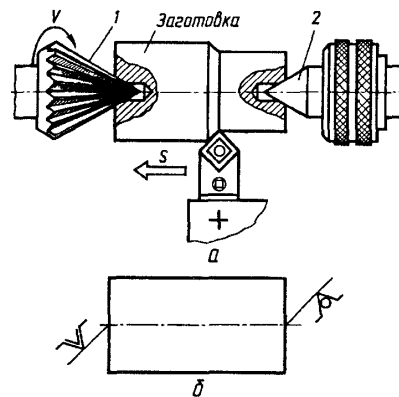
Закріплення заготовки в задньому обертовому центрі:
